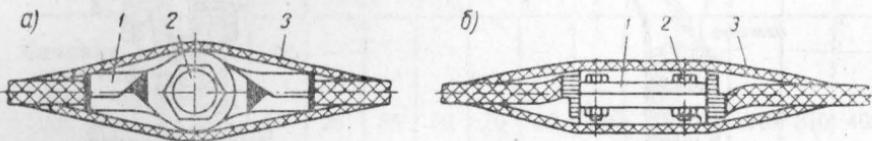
Штепельное соединение сварочных проводов:
